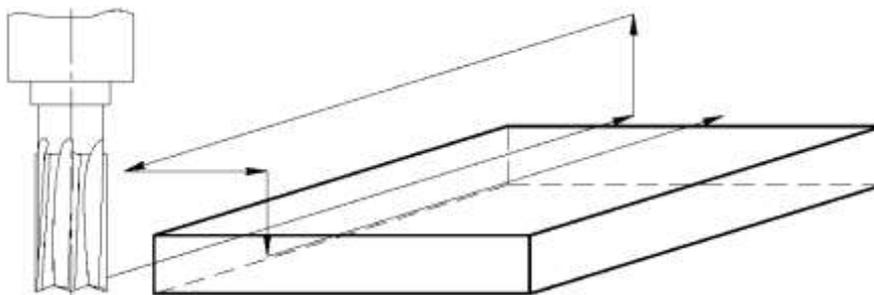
Ш-образный метод удаления припуска и напуска
